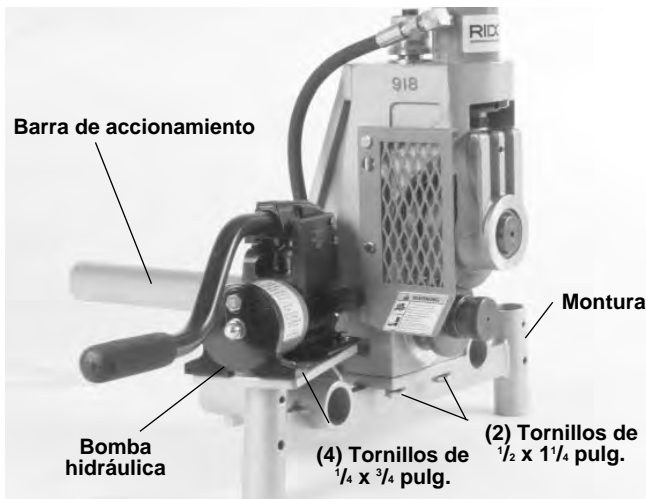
Ranuradora a Rodillos industrial No. 918 montada en la base de la No. 1822
